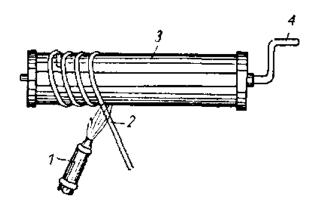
Изготовление спирали из стеклянной трубки: / — газовая горелка; 2—стеклянная трубка; 3— деревянный вал с клиньями; 4—ручка для вращения.
